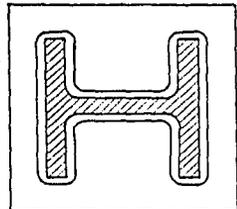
INDICACION DE EXTENSION DE SOLDADURA
